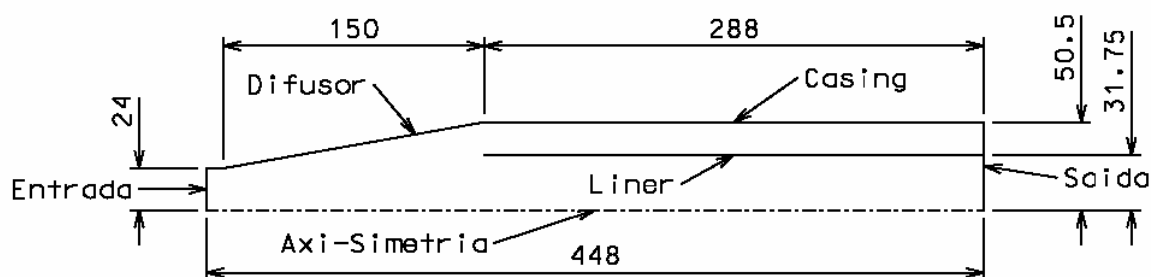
Dimensões do Difusor, Liner e Casing
